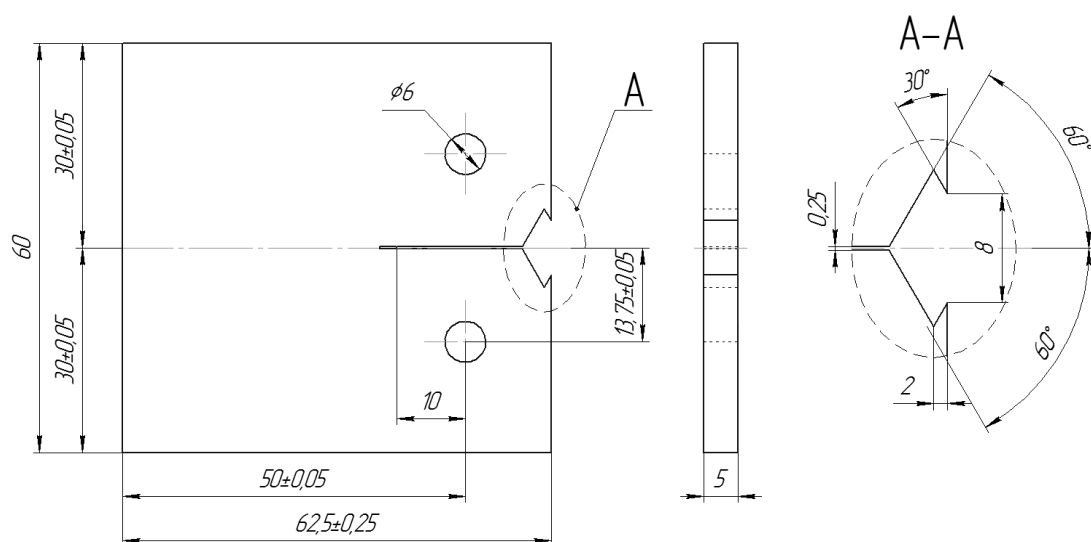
Геометрия нестандартного образца для испытаний
